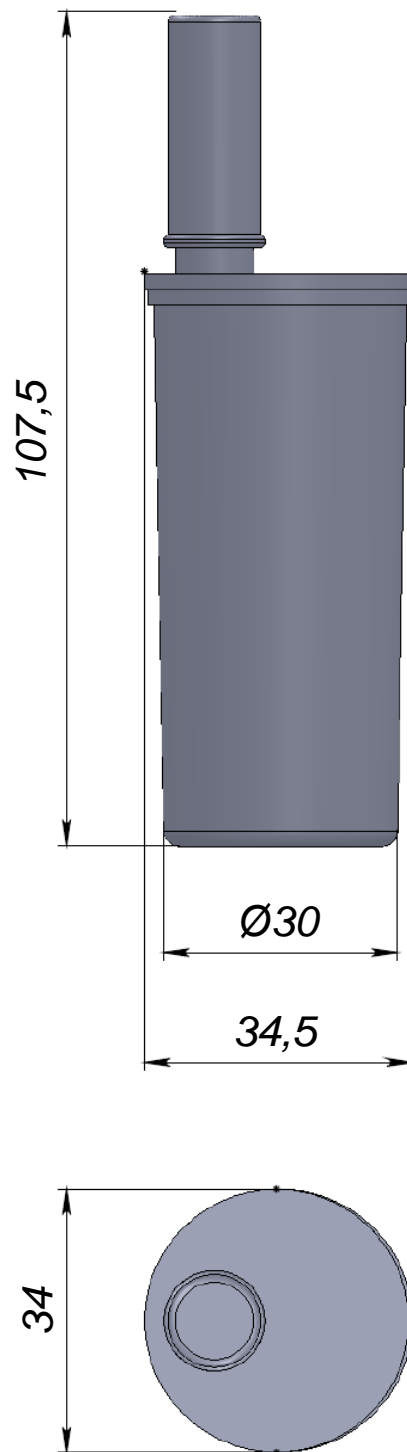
Внешний вид измерителя в сборе, с защитным колпачком и его габаритные размеры
